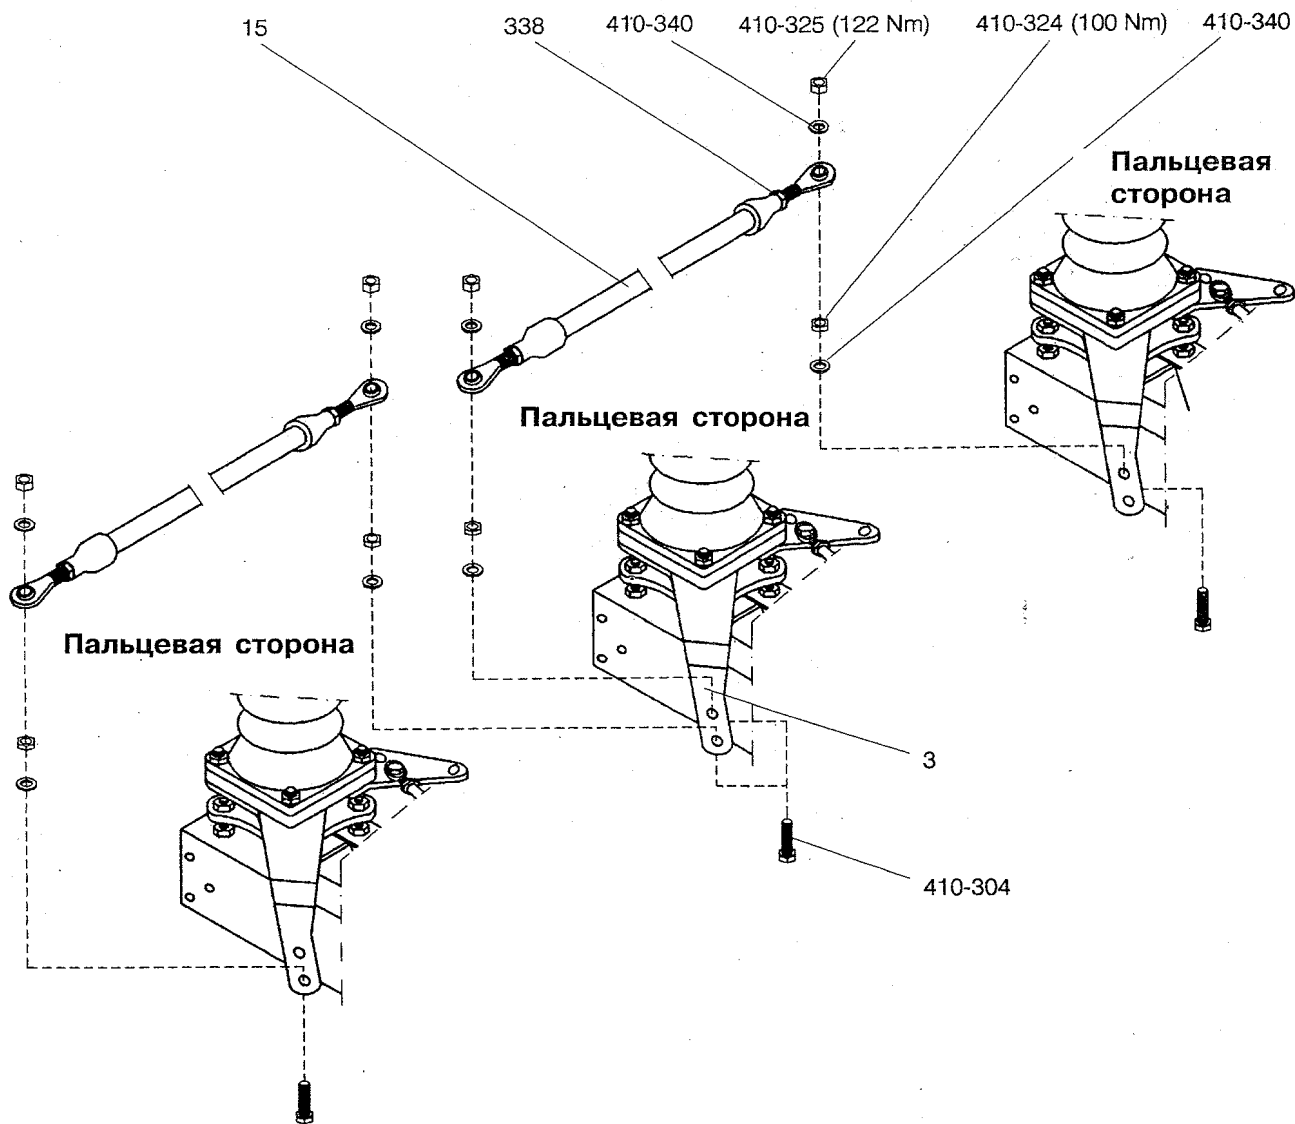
Установка тяг: параллельное расположение полюсов разъединителя
